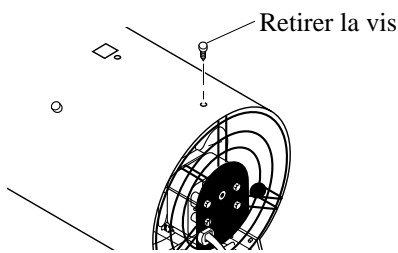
Retrait de la vis du haut de la grille de ventilateur
